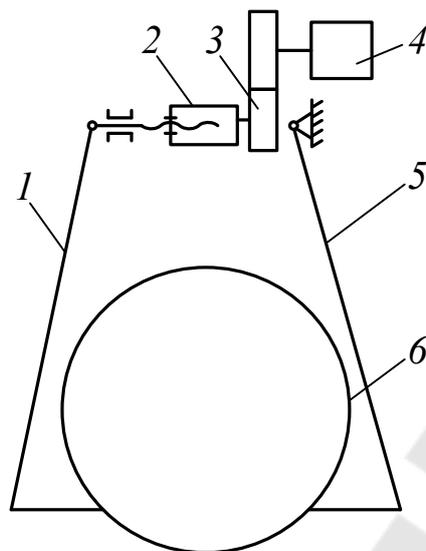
Кинематическая схема механизма захвата: 1 и 5 – захваты; 2 – винтовая передача; 3 – редуктор; 4 – электродвигатель; 6 – труба
